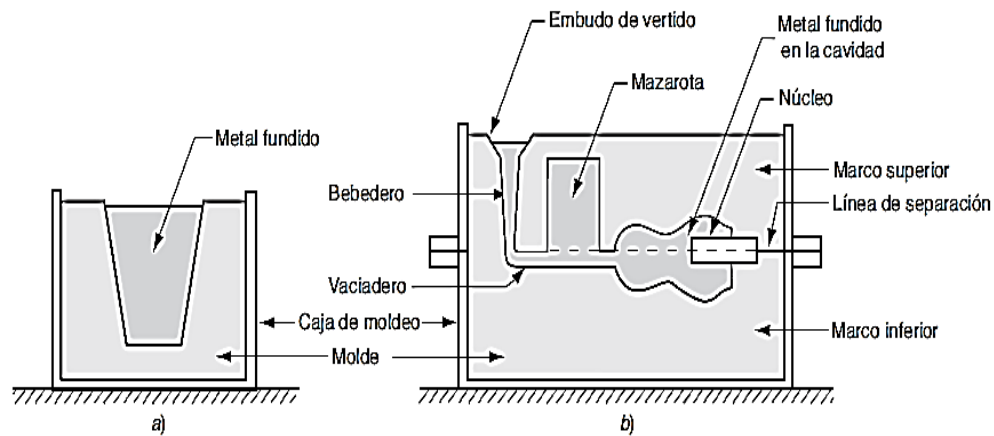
Tipos de moldes a) Molde abierto b) Molde cerrado
